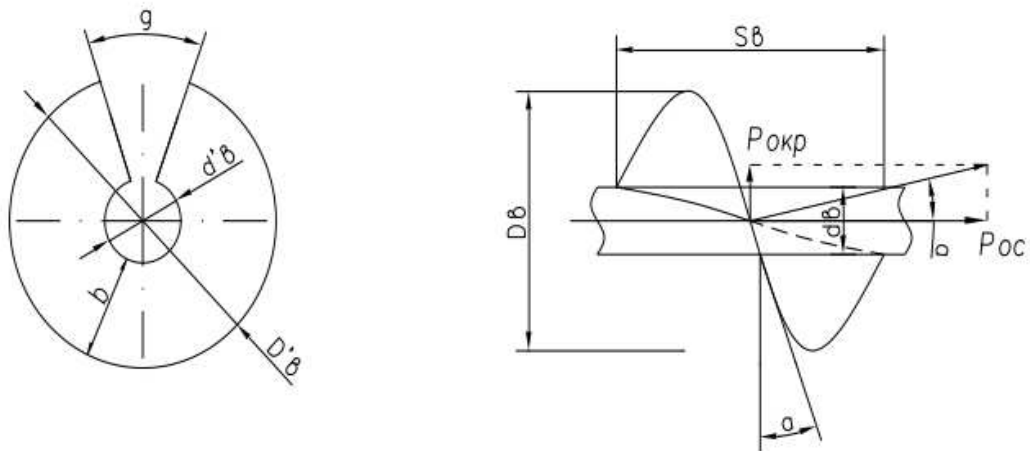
Схема до розрахунку розмірів заготовки шнека
